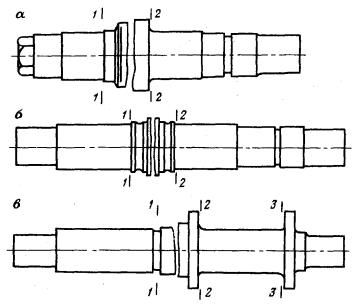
Расположение контролируемых участков на валах центробежных компрессоров:
